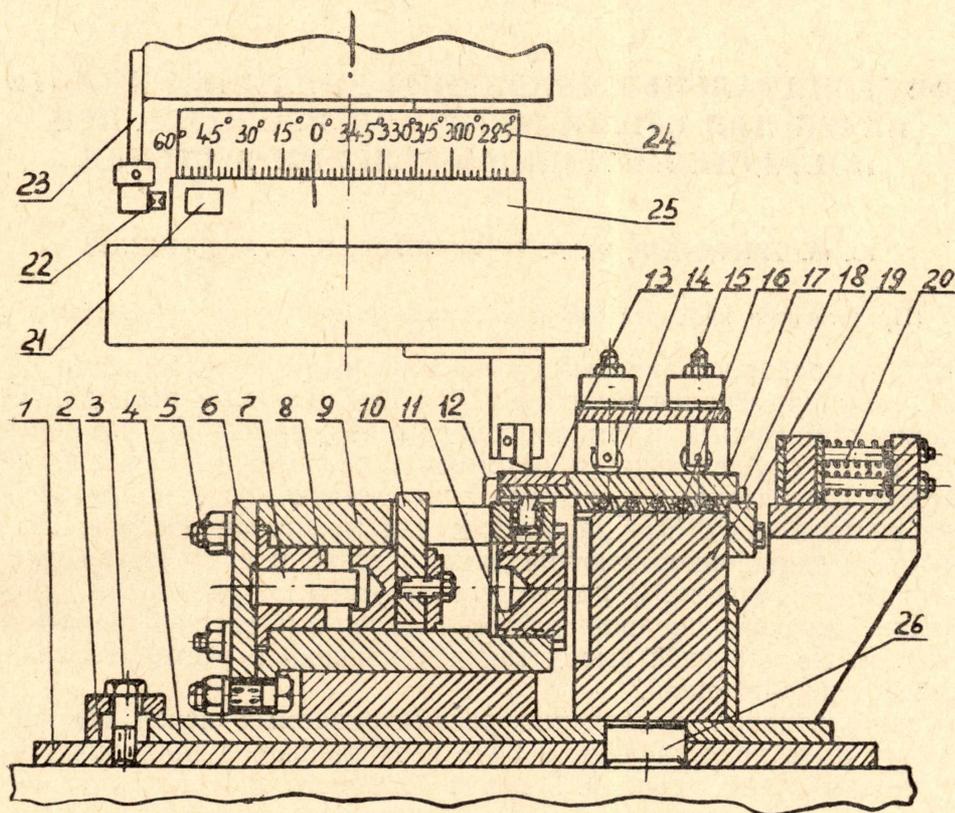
Приспособление для мгновенного останова процесса резания при торцевом фрезеровании
